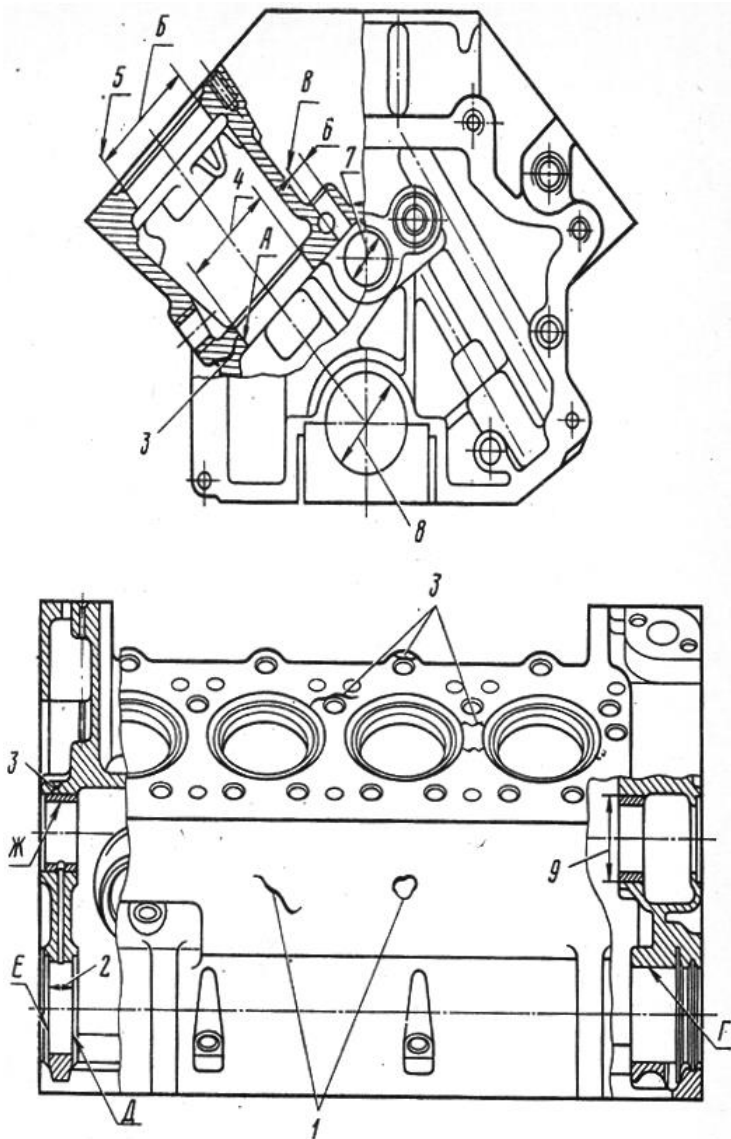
Блок цилиндров двигателя ЗИЛ
